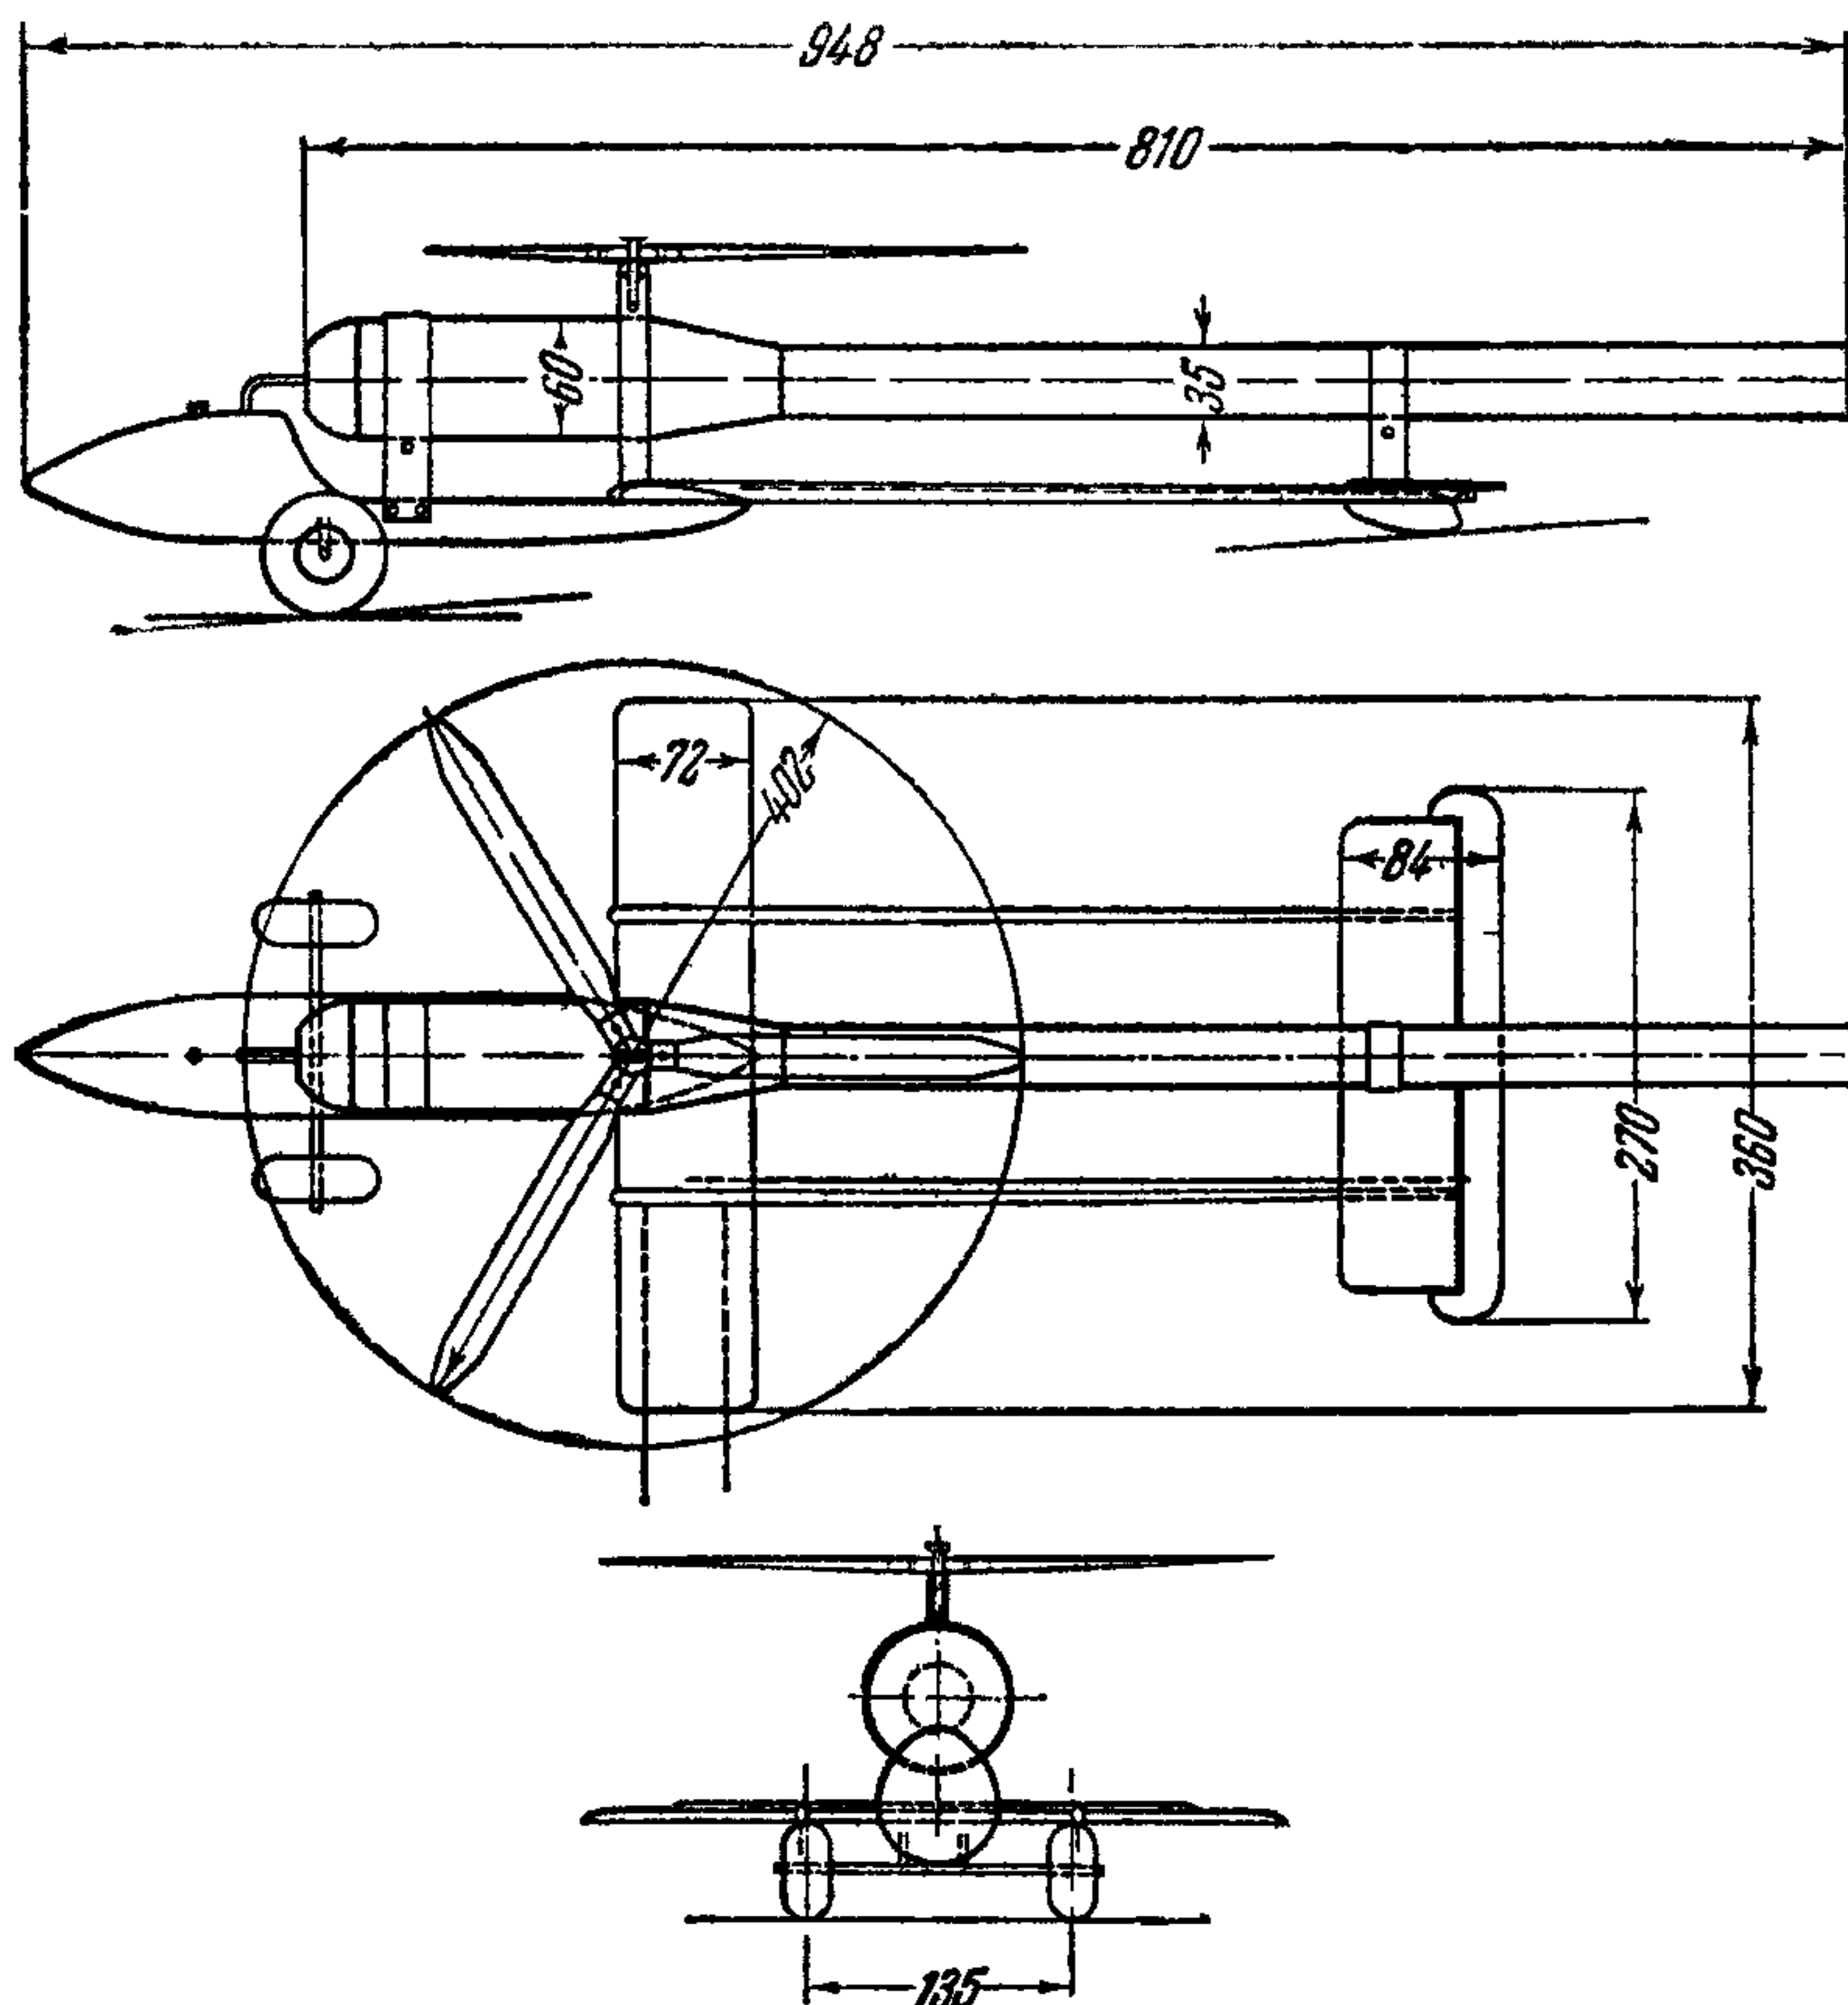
Чертеж реактивной модели автожира В. Шеремета
